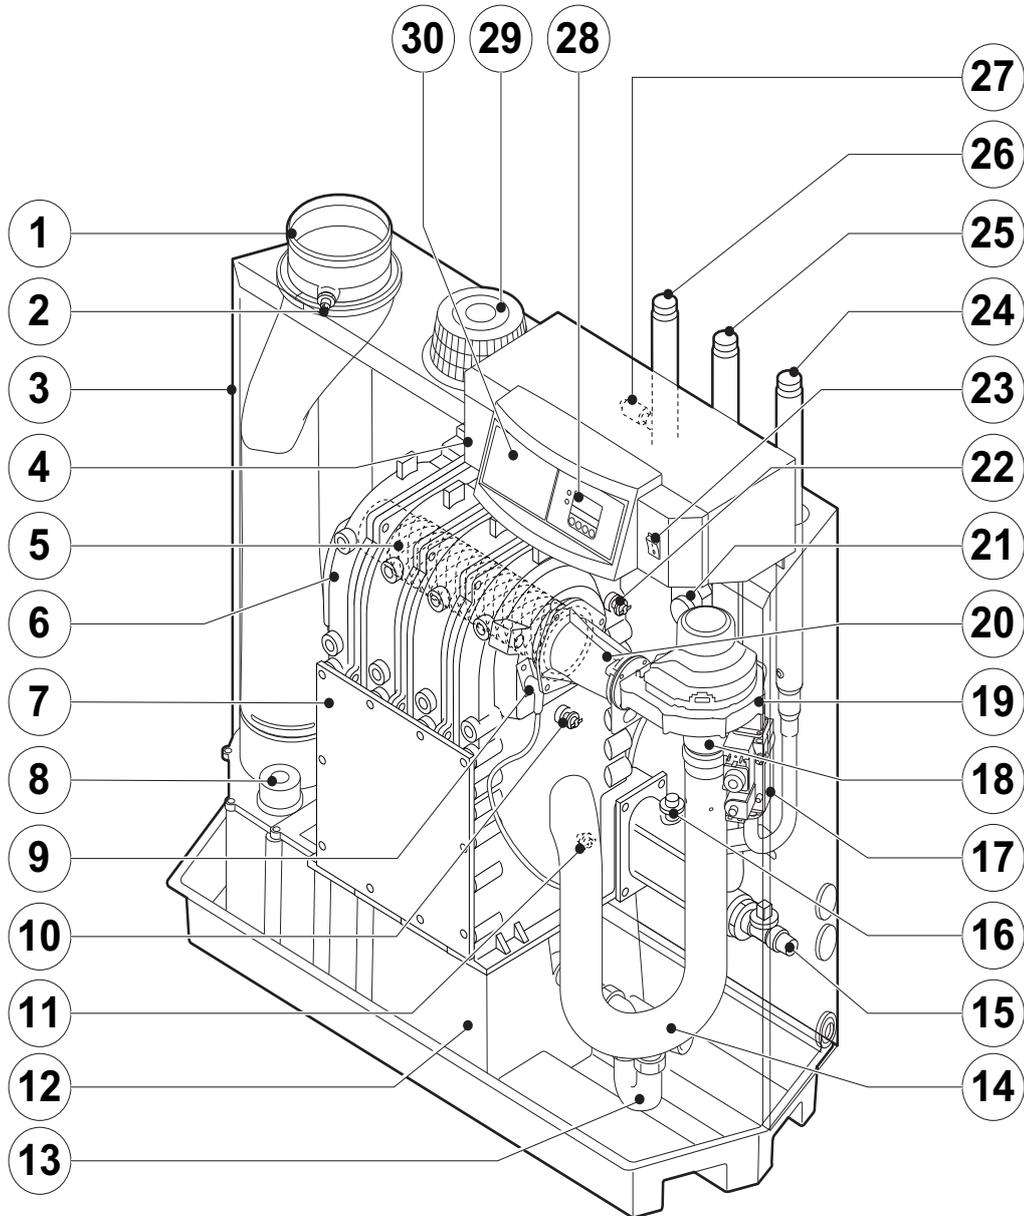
Querschnitt (abgebildet ist die 200-5 Ausführung)
